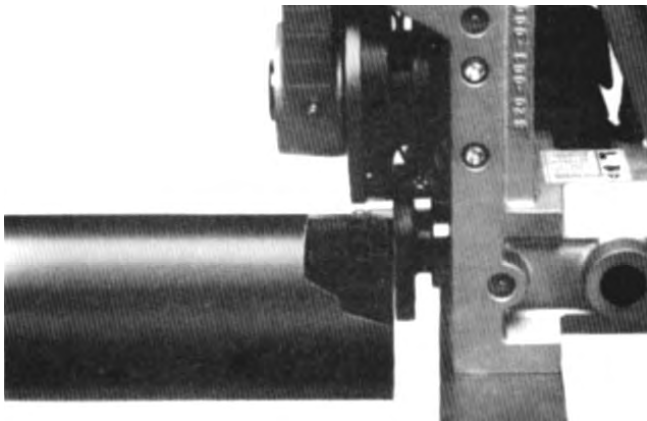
Primer plano del tubo colocado contra el borde del rodillo de accionamiento
